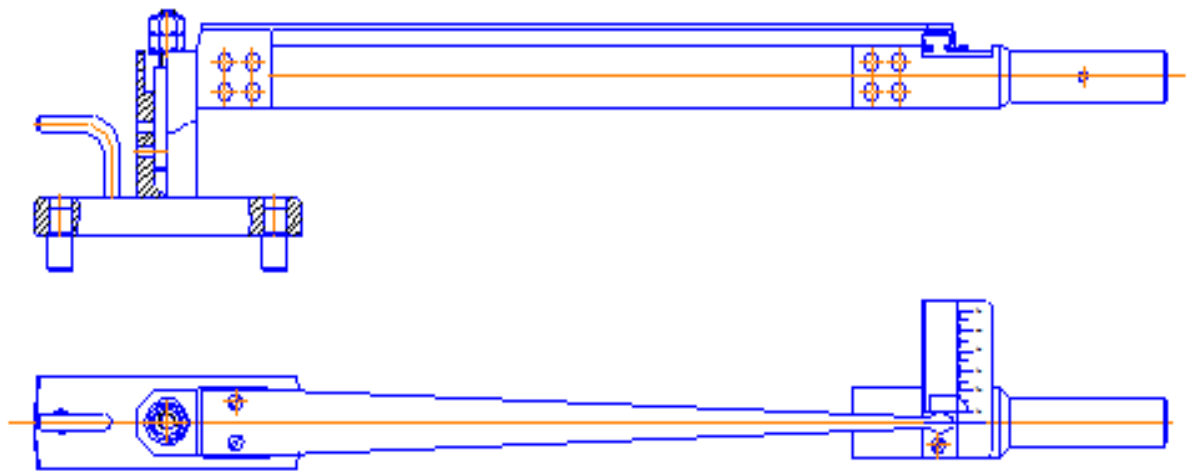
Пристосування для контролю зусилля провертання колінчастого вала двигуна
